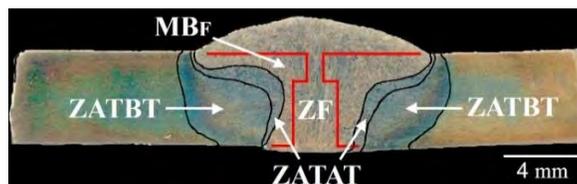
Zonas del cordón de soldadura utilizadas para la cuantificación de áreas. Metal base fundido MB_F.
